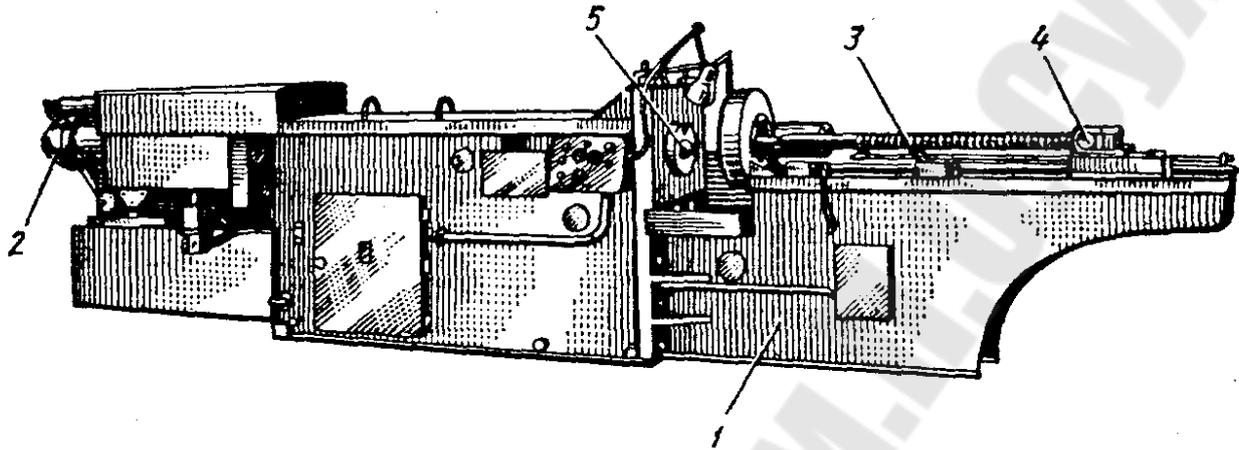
Общий вид горизонтально-протяжного станка
